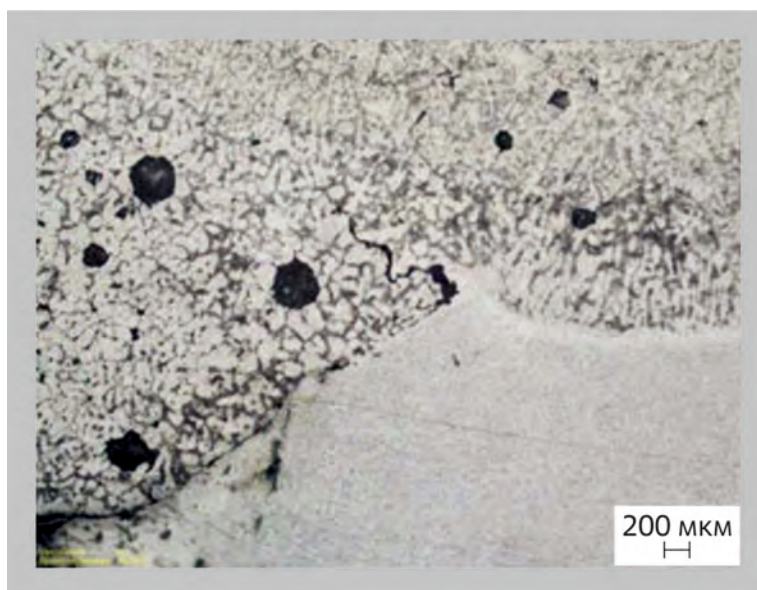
Внешний вид дефектов в виде пор и окисных включений в сварных швах алюминиевых сплавов
